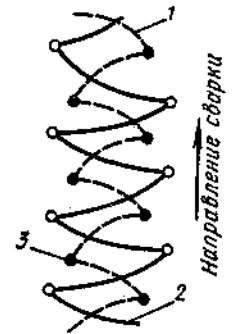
Движения горелки и проволоки при сварке угловых валиковых швов:
